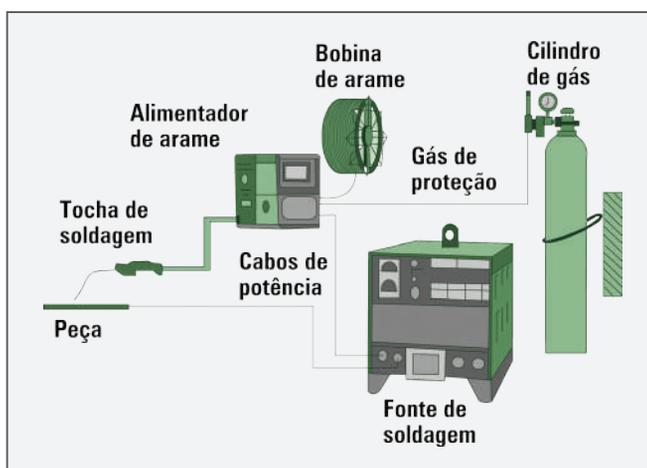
Equipamentos básicos da soldagem MIG/MAG
